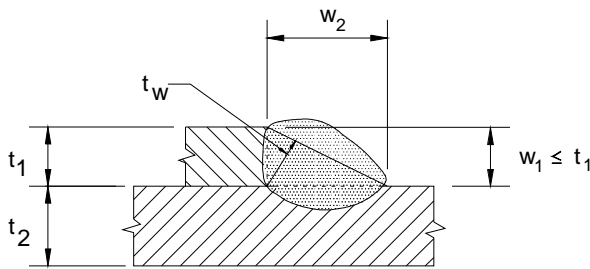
A Soldaduras de filete - Unión solapada
